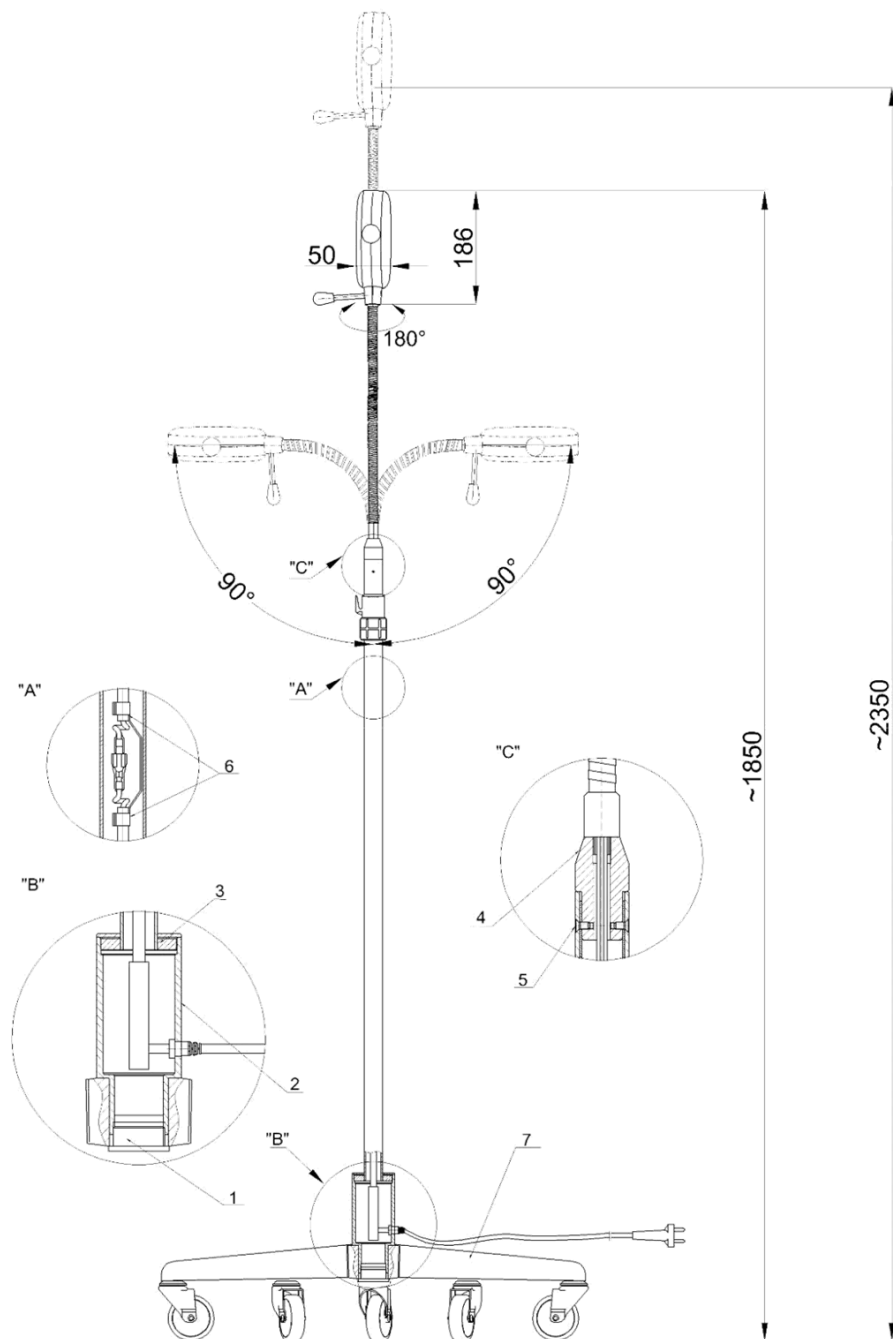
Pripojenie komponentov vyšetrovacieho svetla SOLIS 30W
